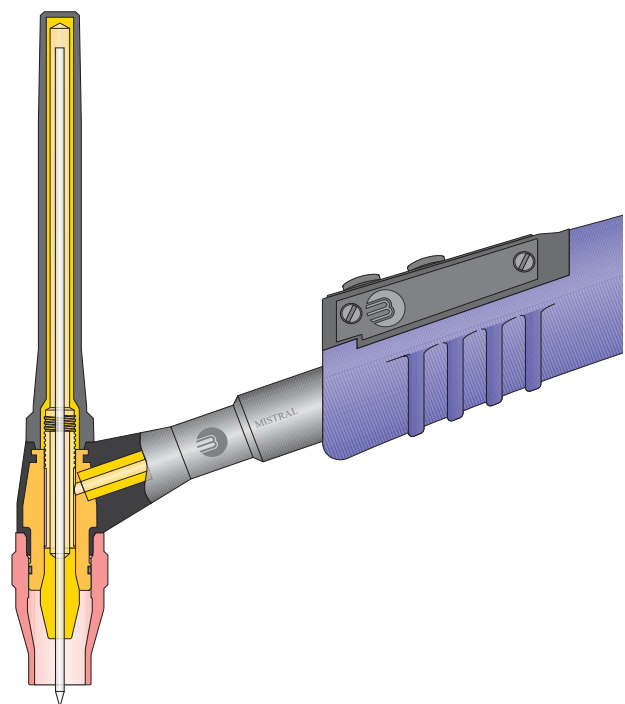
Сварочная горелка ВИГ с газовым охлаждением
